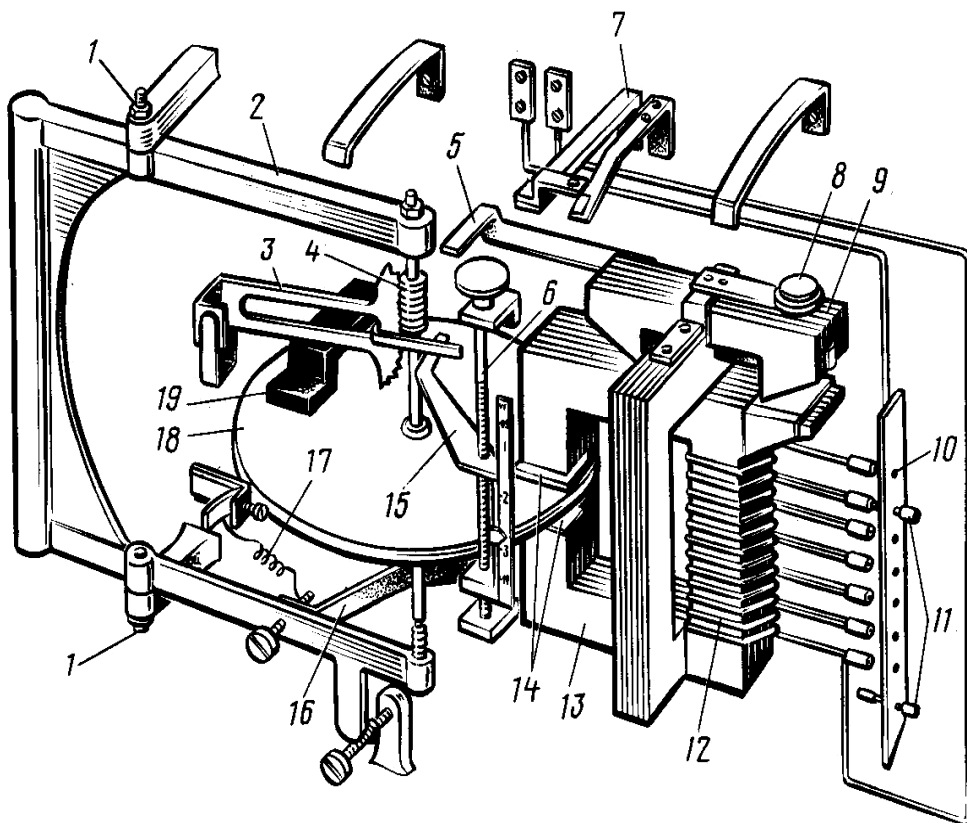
Конструкція індукційного струмового реле РТ-80:
